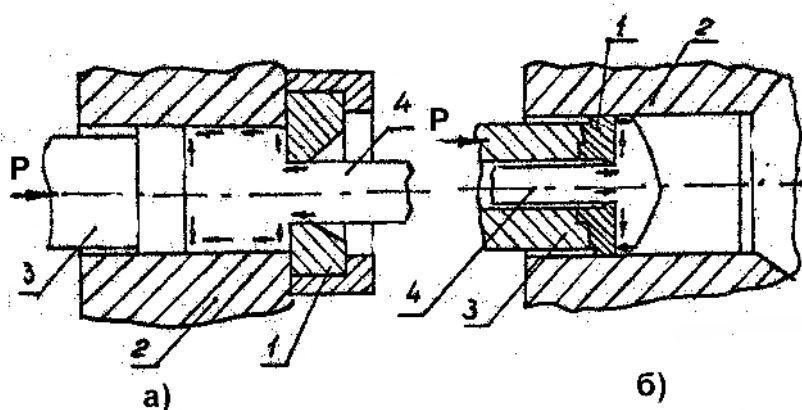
Схемы прямого (а) и обратного (б) прессования.
